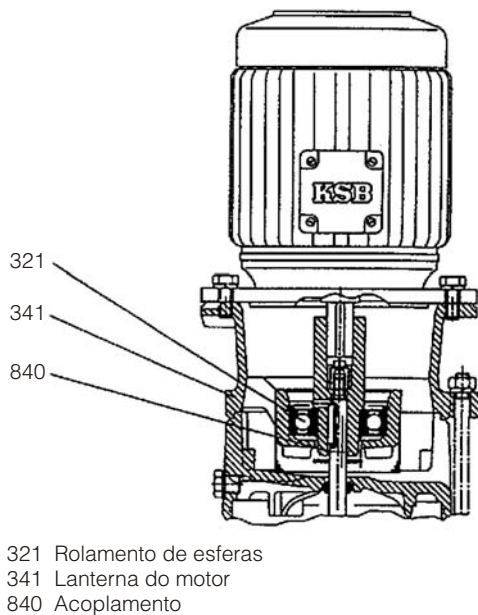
Lanterna do motor com rolamento e acoplamento
